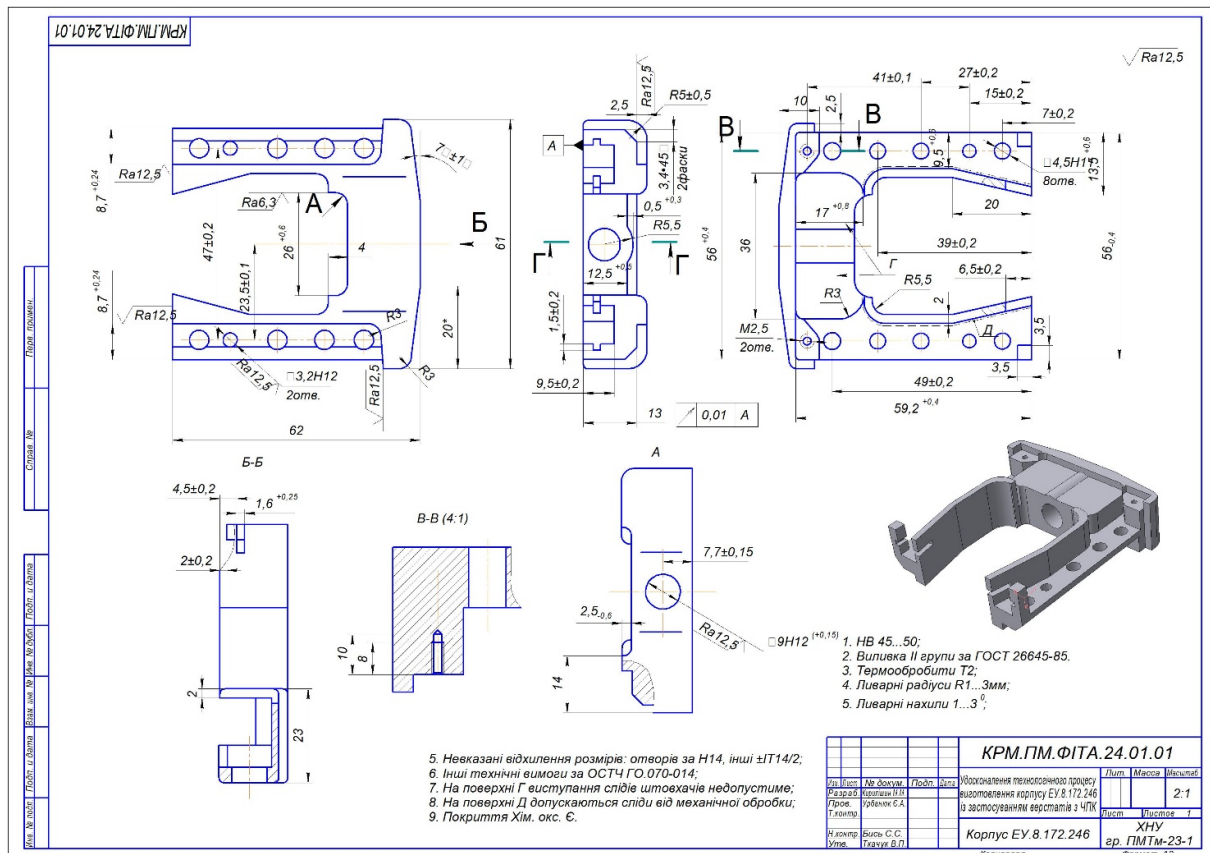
Кресленник деталі «Корпус ЕУ.8.172.246»
